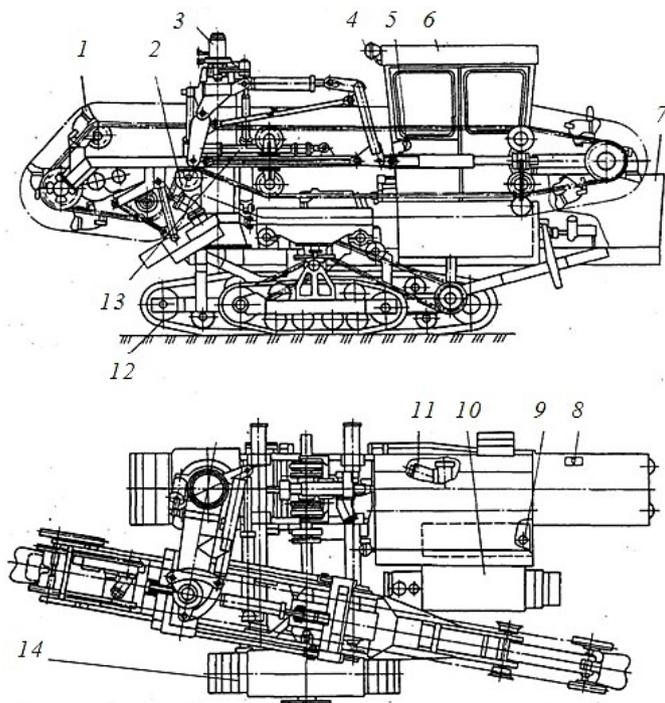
Общий вид каналоочистителя МР-15 в транспортном положении: 1 — рабочий орган; 2 — метатель; 3 — пилон; 4 — освещение; 5, 10, 13 — гидроцилиндры; 6 — кабина; 7 — капот; 8, 9, 11 — гидромоторы; 12 — основная гусеница; 14 — дополнительная гусеница
